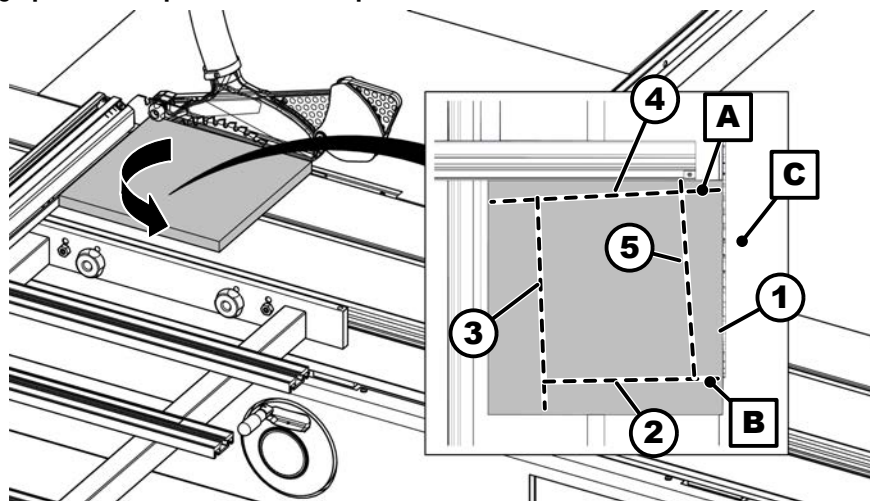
Coupe d'essai - coupe de 5 côtés
